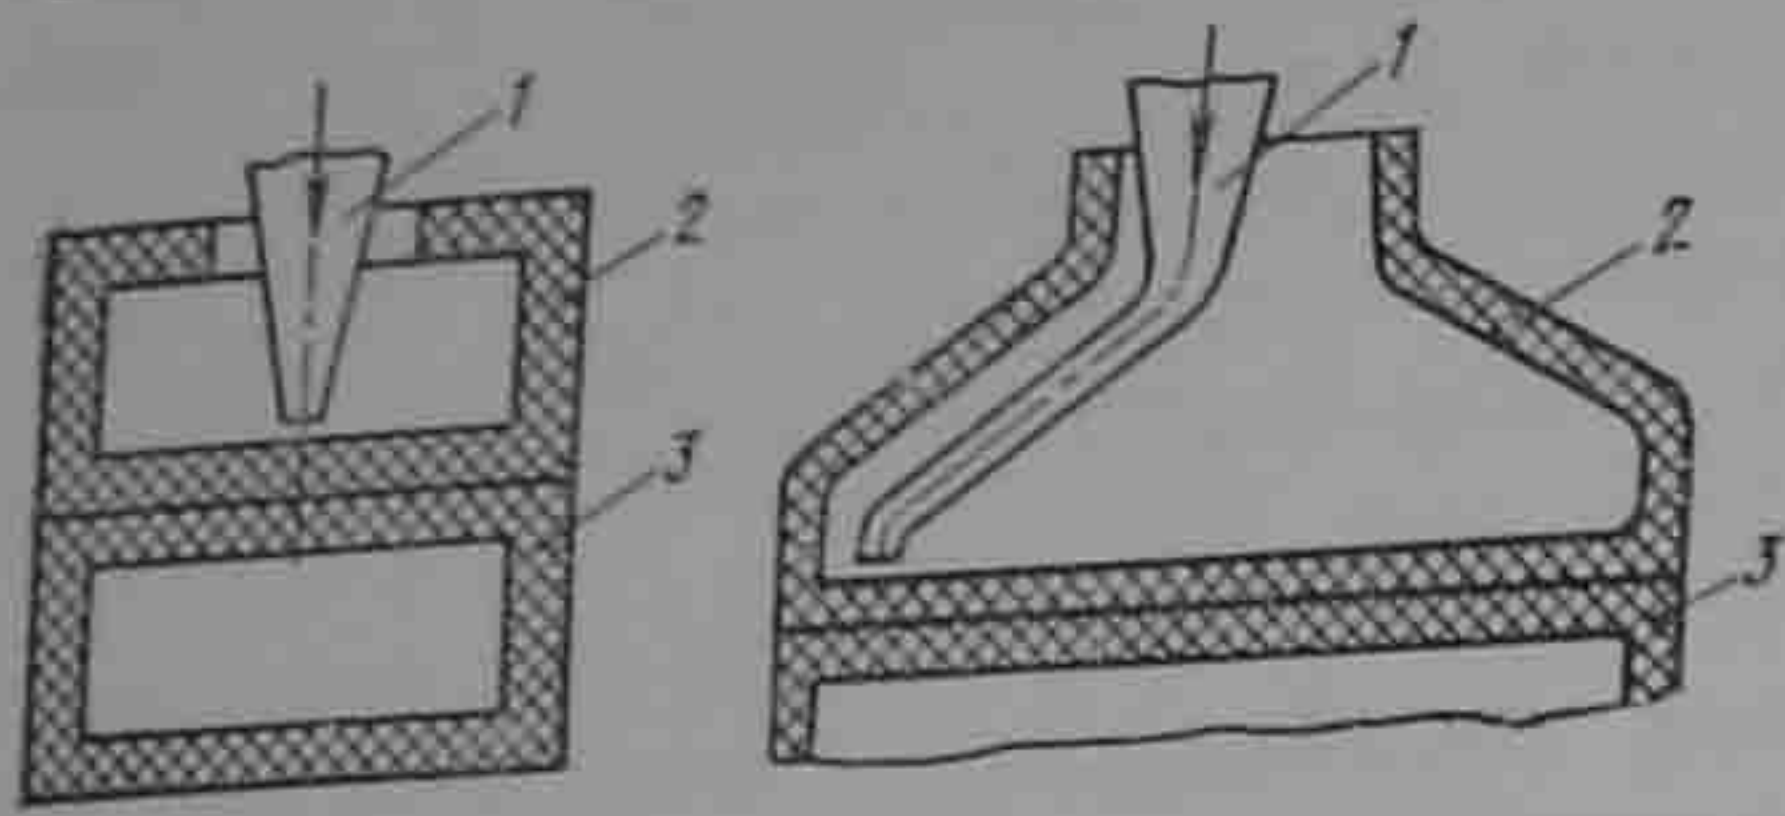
Схемы ультразвуковой сварки в труднодоступных местах:
